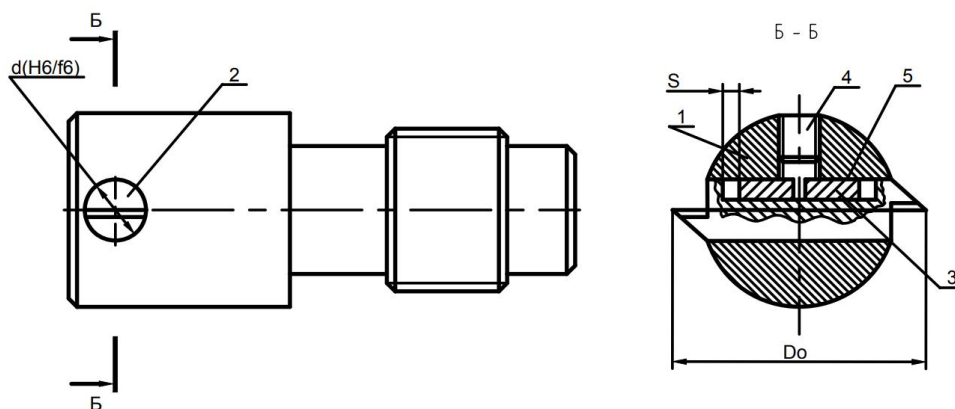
Плавающая головка для чистового растачивания отверстий
